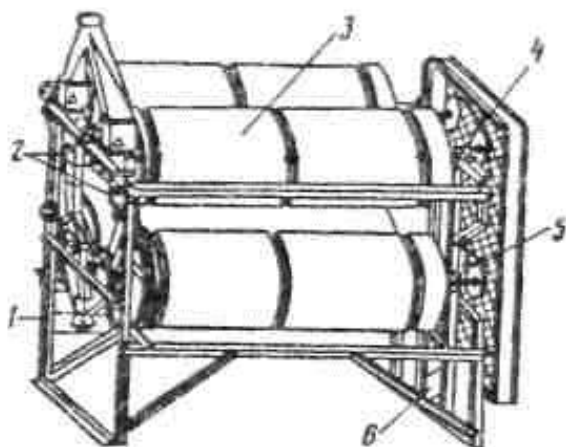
Триерный блок ЗАВ-10.90.000: 1 - рама; 2 - передние распределители; 3 - триерный цилиндр; 4 - верхний контрпривод; 5 - нижний контрпривод; 6 - задний распределитель.
